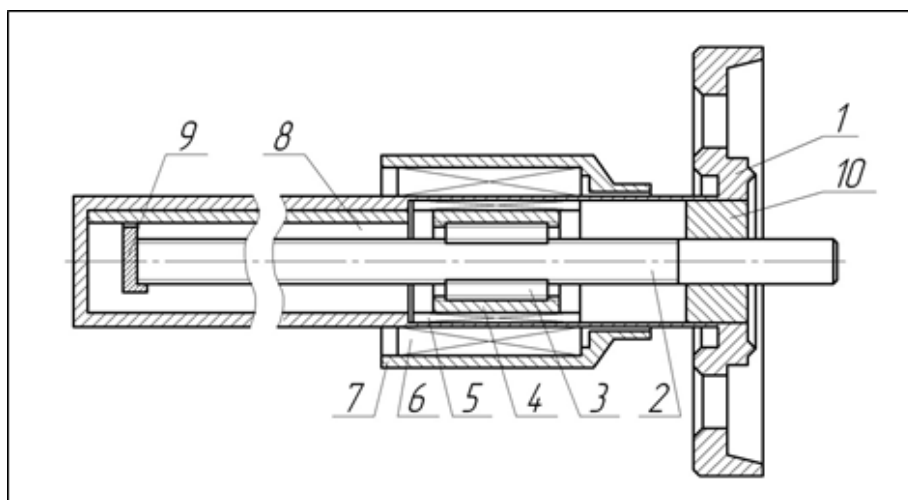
Планетарный резьбовой ввод движения в вакуум с магнитной муфтой: 1 – герметичный корпус; 2 – винт; 3 – ролики; 4 – охватывающая гайка с кольцевыми канавками; 5 – внутренний магнит; 6 – наружный магнит; 7 – входное звено вращательного движения; 8 – шпонка; 9 – ползун; 10 – направляющая
